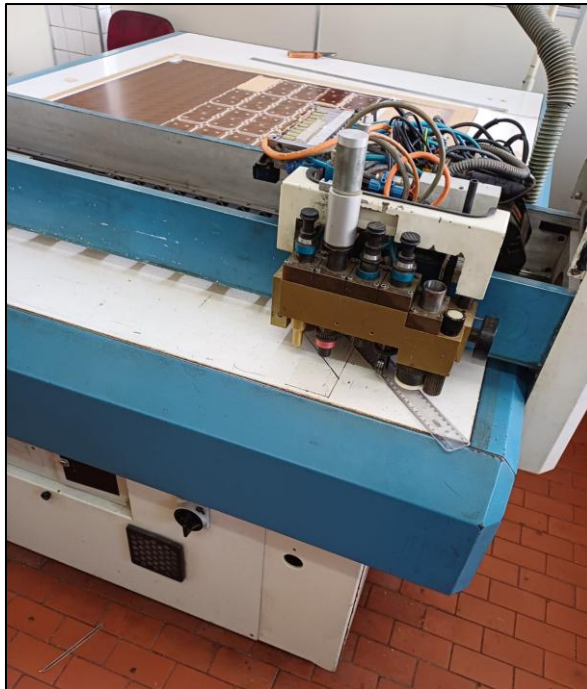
Vista geral da máquina para fresagem de placa fenólica.
